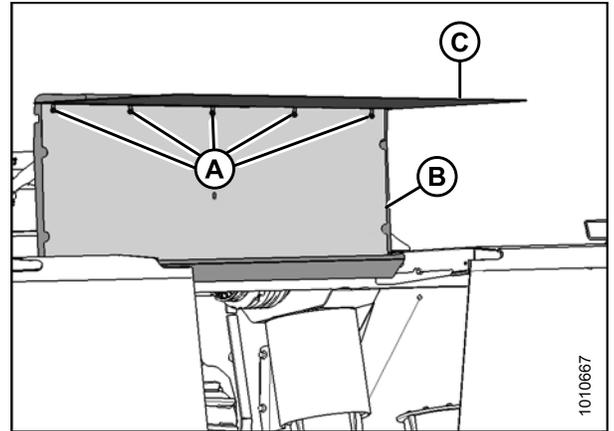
Écrous fixant le panneau de protection et le rideau à la porte de la barre de coupe
